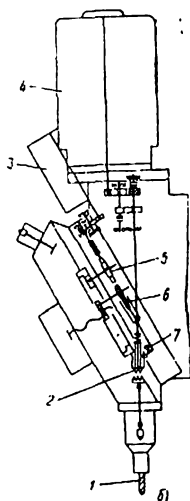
Кінематична схема рушія РГ з обертальними шпинделями:
